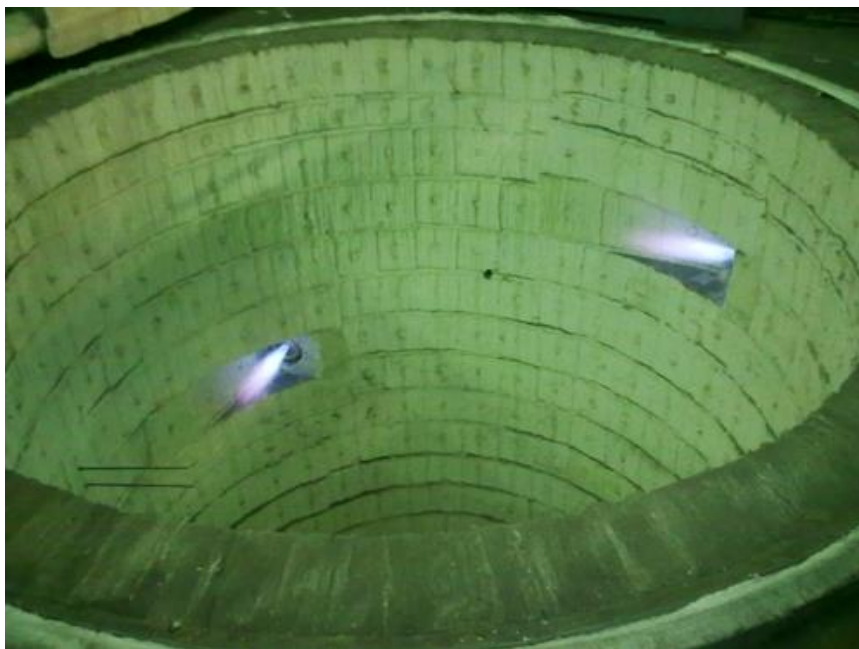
Общий вид футеровки печи керамо-волокнистыми блоками и установка горелок
